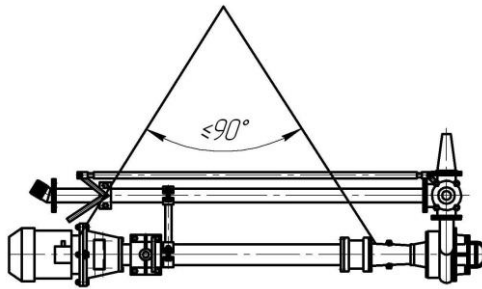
Схема стропування на монтажному кресленні насосного агрегата
